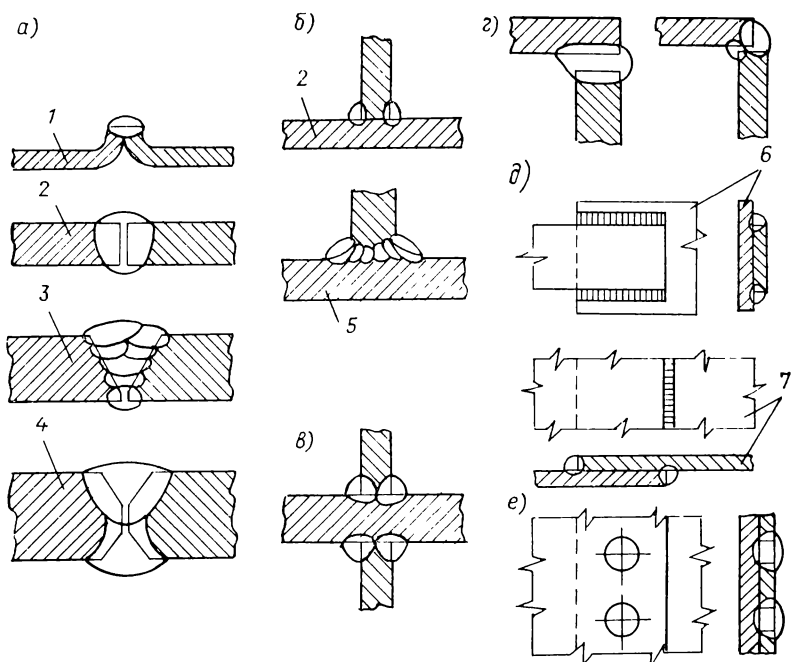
Типы сварных соединений: а — стыковые; б — тавровые; в — крестовое; г — угловые; д — нахлесточное; е — нахлесточное с электродзащелками.
